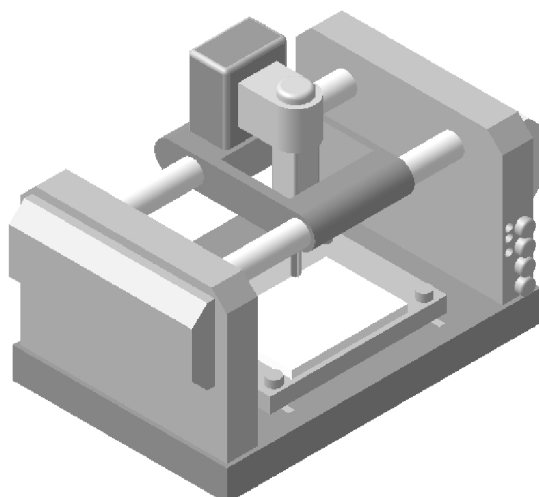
Настольный фрезерный станок с ЧПУ
